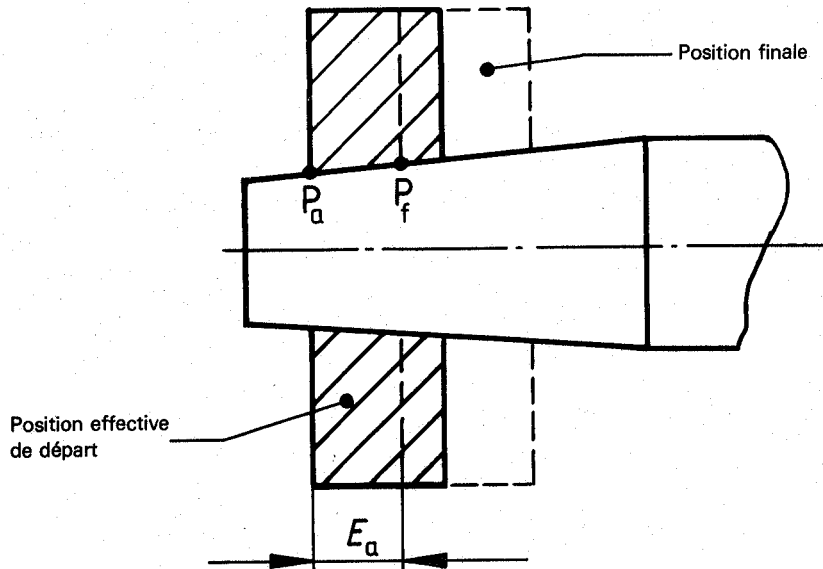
Ajustement conique avec serrage réalisé par assemblage forcé jusqu'à une dimension-repère
